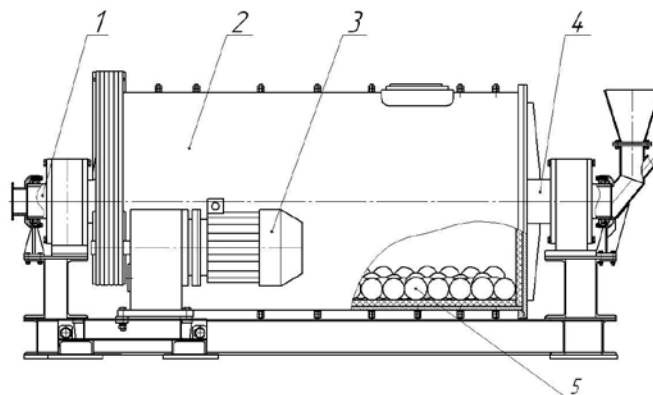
Шаровая трубная мельница: 1 – разгрузочная цапфа; 2 – корпус; 3 – привод; 4 – загрузочная цапфа; 5 – мелющие шары
